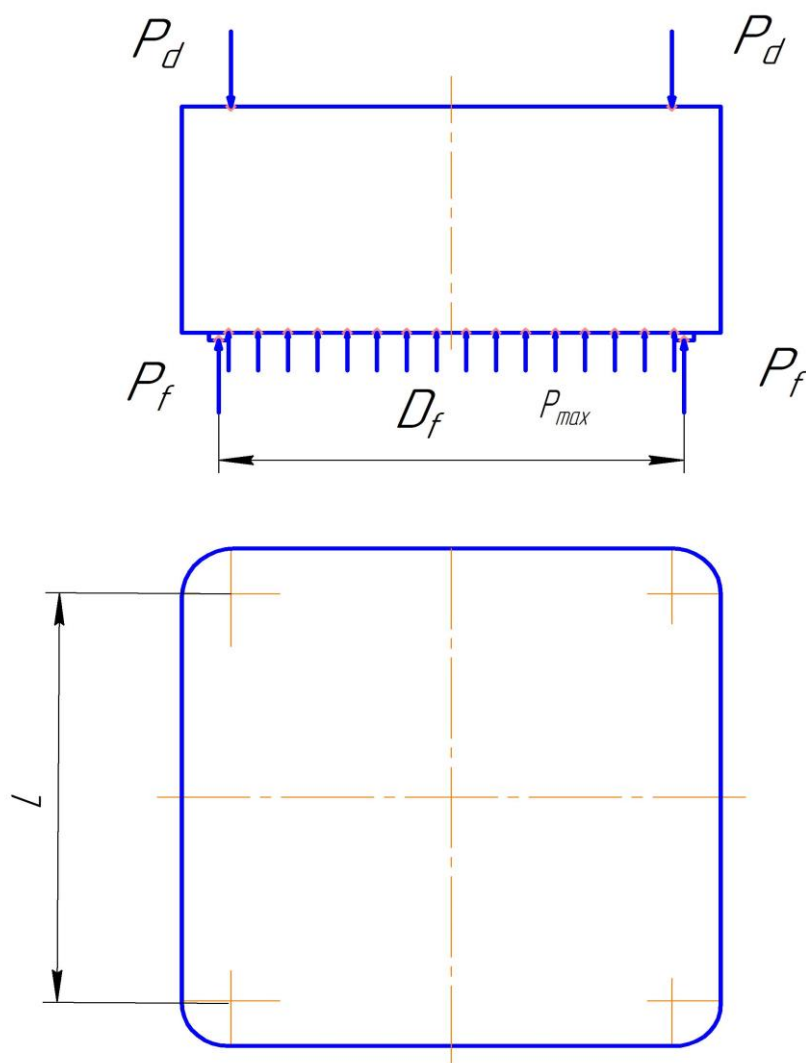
Розрахункова схема кришки робочого циліндру
